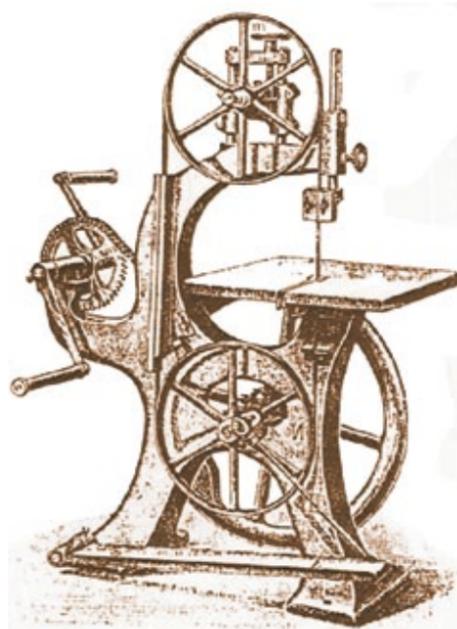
Столярный ленточно-пильный станок конца XIX века с ручным приводом обращения пилы
